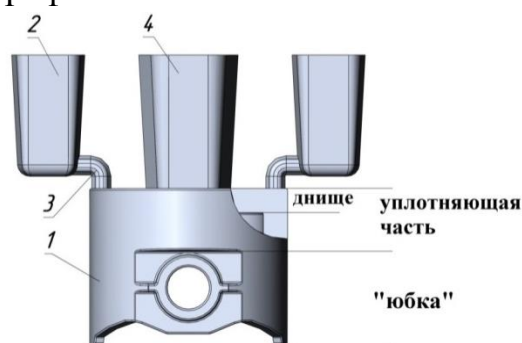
Поршень двигателя легкового автомобиля с элементами литейной формы: 1 – отливка «Поршень»; 2 – литниковая чаша; 3 – стояк; 4 – прибыль
